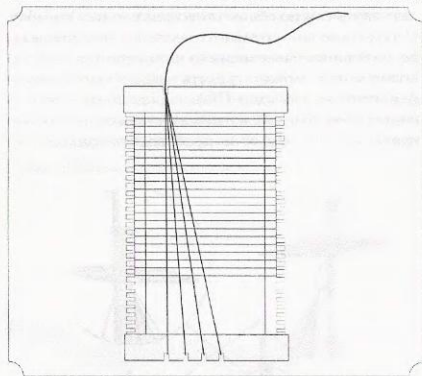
Приспособление для изготовления вант миниатюрной модели
